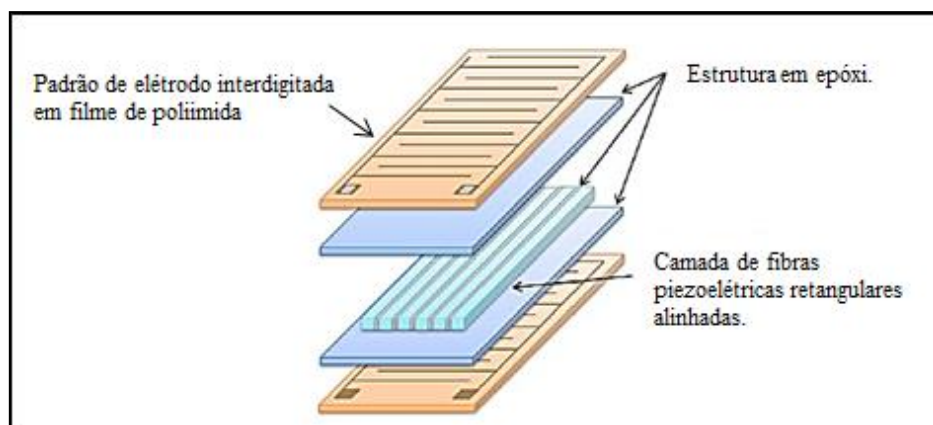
Vista explodida de um MFC da Smart Materials Corporation.
